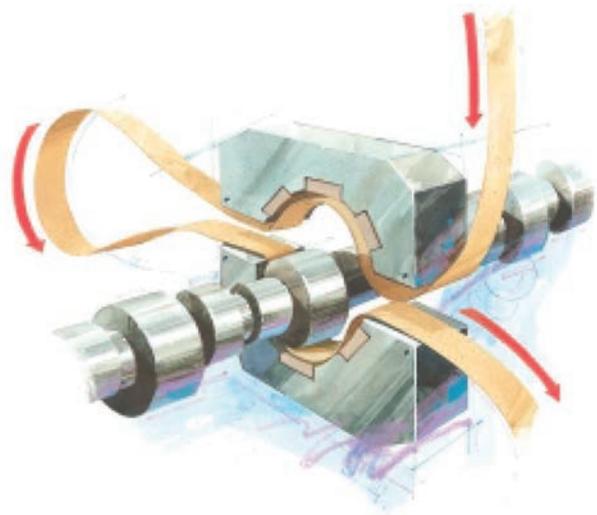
GBQ®-Prozess – Filmführung mit Werkzeug-Schuh
